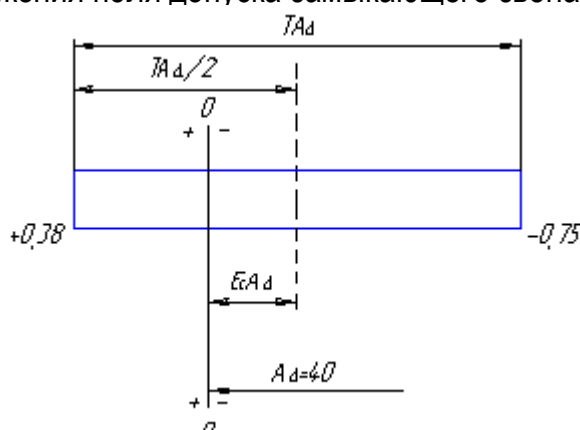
Схема расположения поля допуска замыкающего звена
